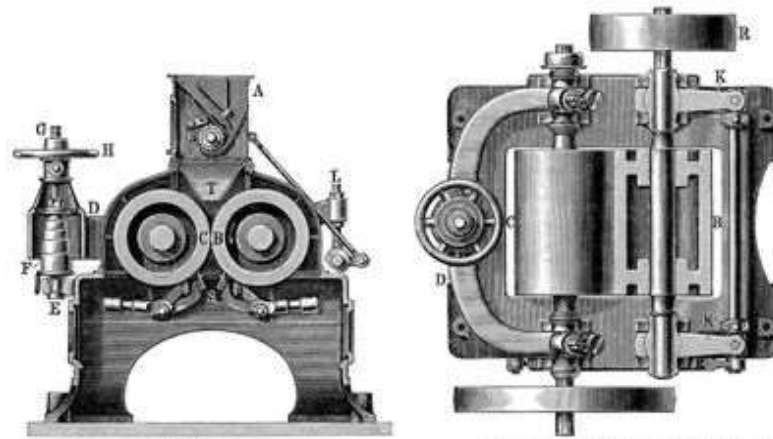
Загальний вигляд вальцевого верстата.
